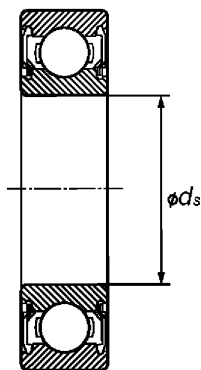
Сечение подшипника качения с уплотнениями
